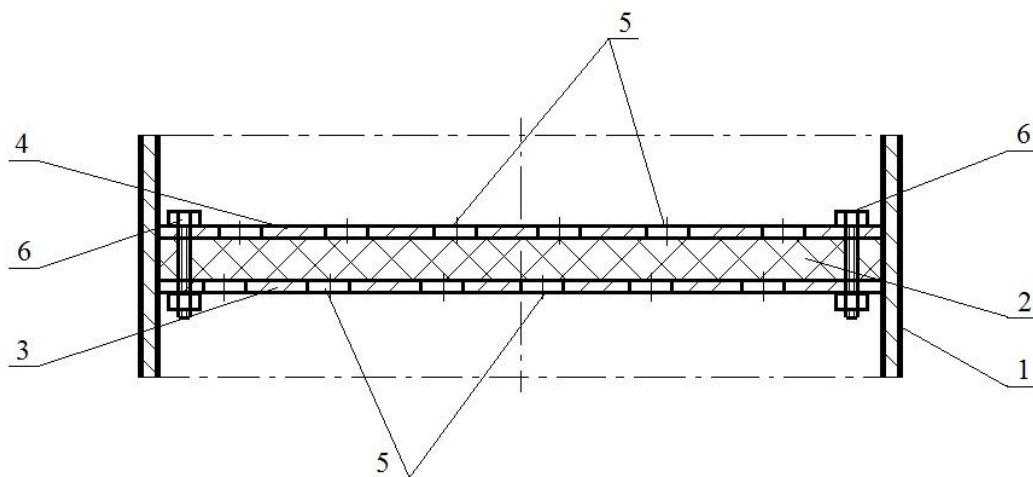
Схема конструкции поропластовой тарелки провального типа [5]:
